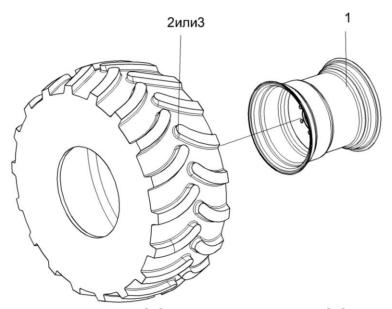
Колесо УЭС-7-0110000-04 и УЭС-7-0110000-05
